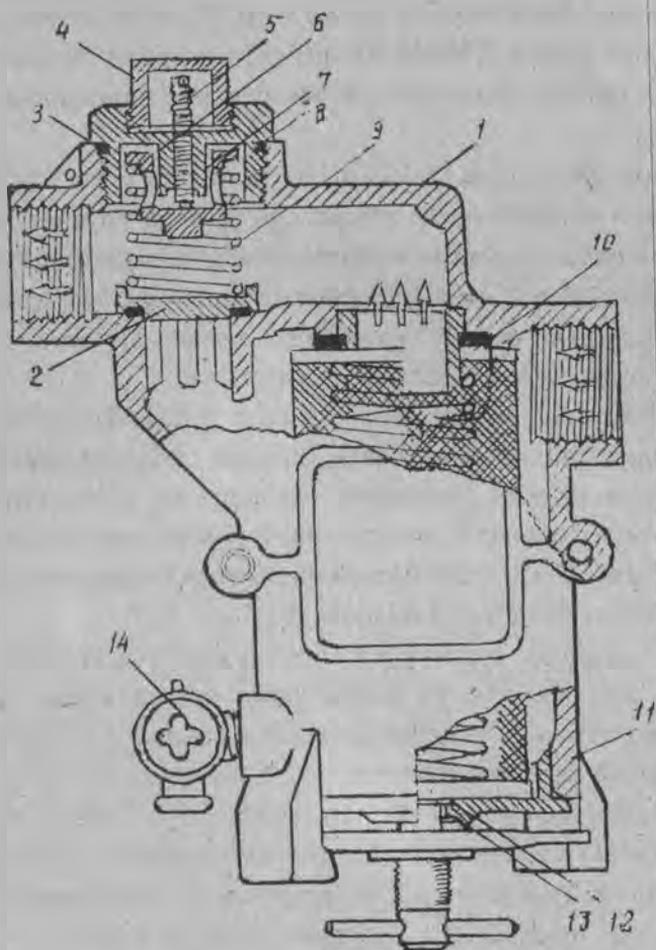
Фильтр тонкой очистки топлива 12ТФ29-1: 1 — корпус; 2 — предохранительный клапан; 3 — прокладка; 4 — колпачок; 5 — регулировочный винт; 6 — гайка; 7 — направляющая; 8 — прокладка; 9 — пружина предохранительного клапана; 10 — фильтрующий элемент (бумажный или металлический); 11 — крышка; 12 — шайба запорная; 13 — гайка; 14 — сливной кран
